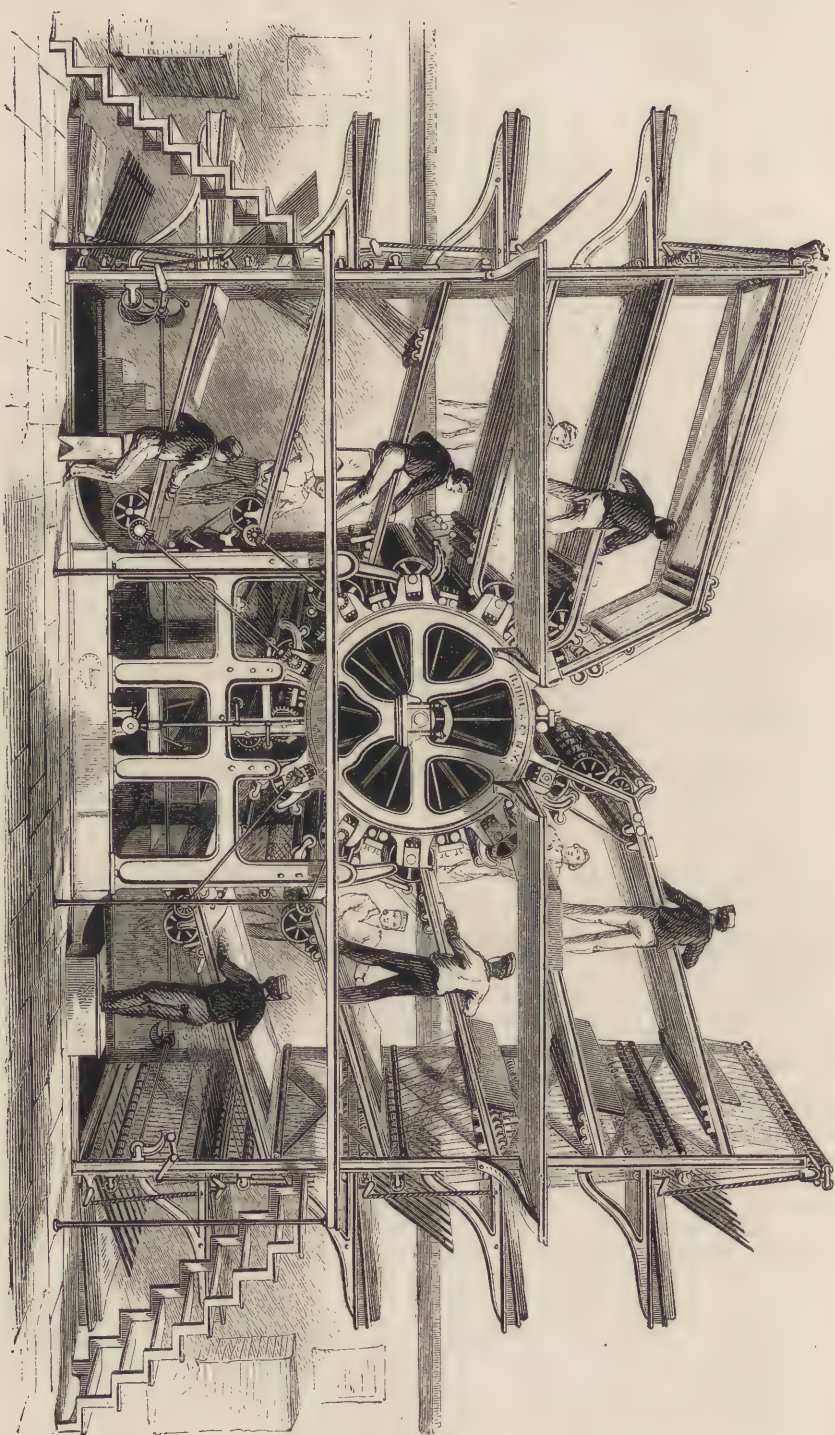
MACHINE CYLINDRIQUE A DIX MARGEURS.
